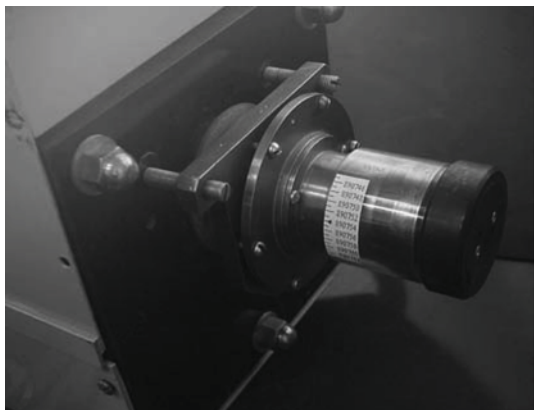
Усовершенствованный механизм перемещения зеркала резонатора, установленный на юстировочном узле лазера
